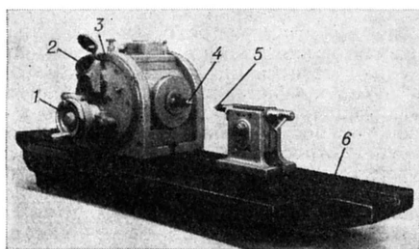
Делительная головка: 1 — блок настройки; 2 — оптический окуляр; 3 — шкала; 4 и 5 — центры для установки детали; 6 — стол.
